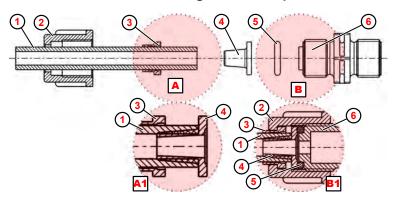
Rohr- Schlauchanschluss mit Kegelteil
